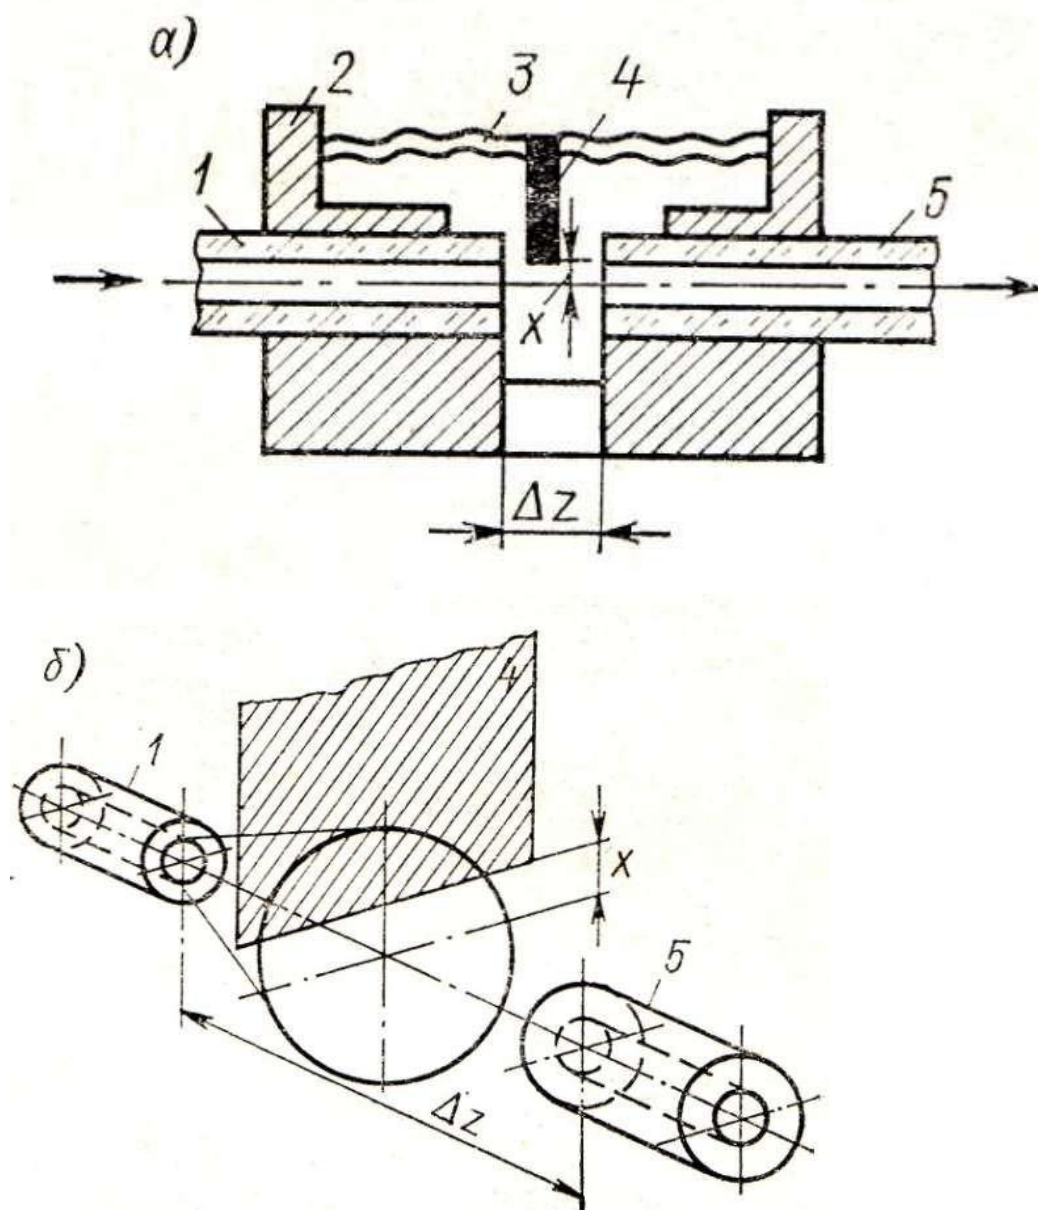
Конструкция шторочного датчика – а; оптическая схема шторочного датчика – б.
